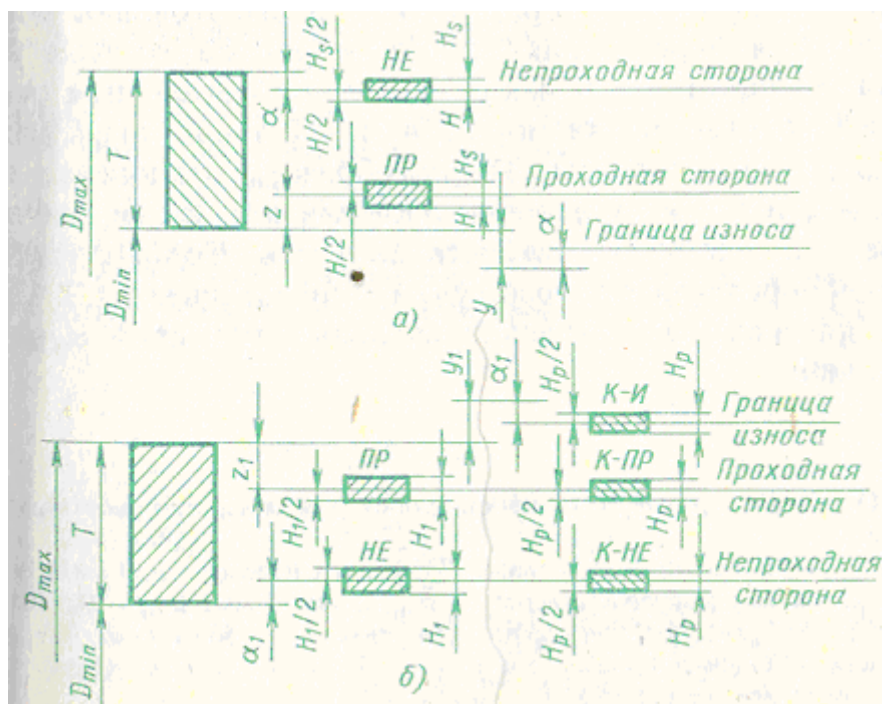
Схема расположения полей допусков калибров:
